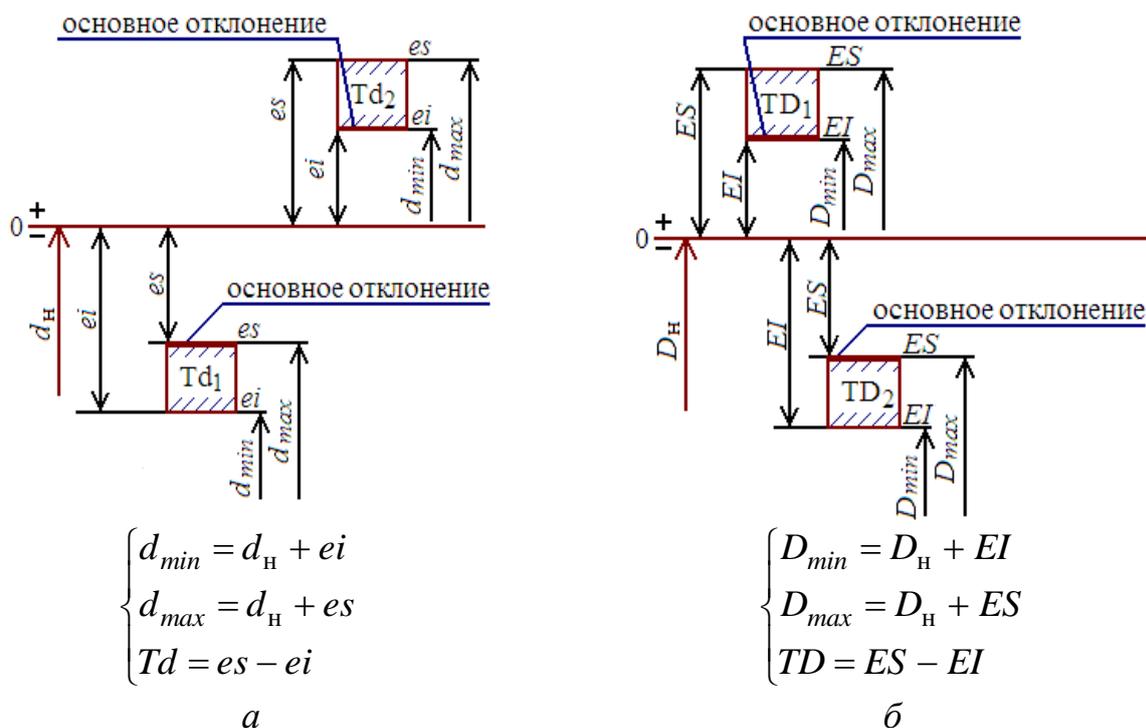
Расположение полей допусков валов – а и отверстий – б
